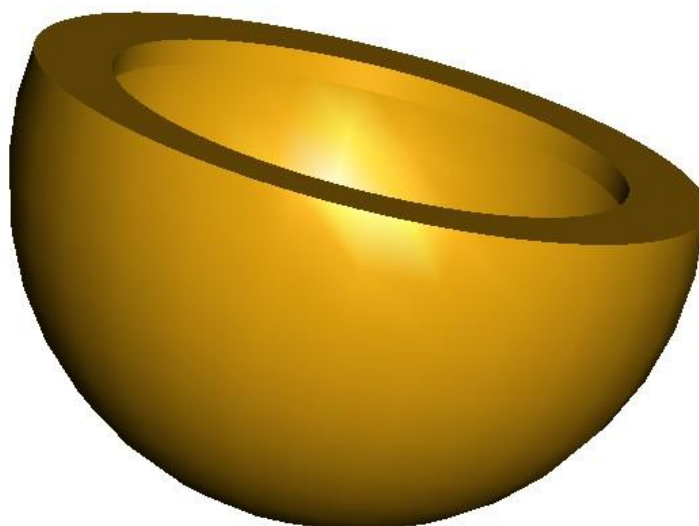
Konstrukční uspořádání impaktoru dětské hlavy [12]
